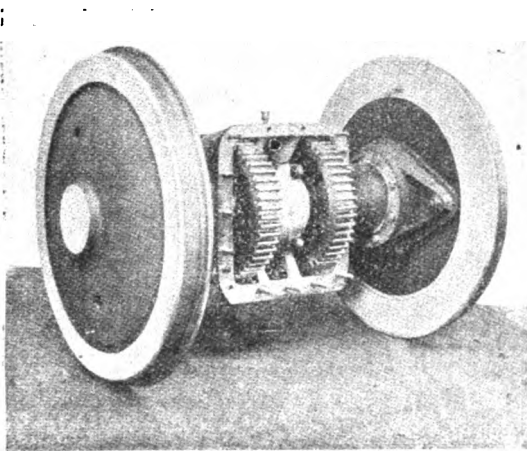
Vue de l'essieu moteur et du train d'engrenages qui commande les roues.
